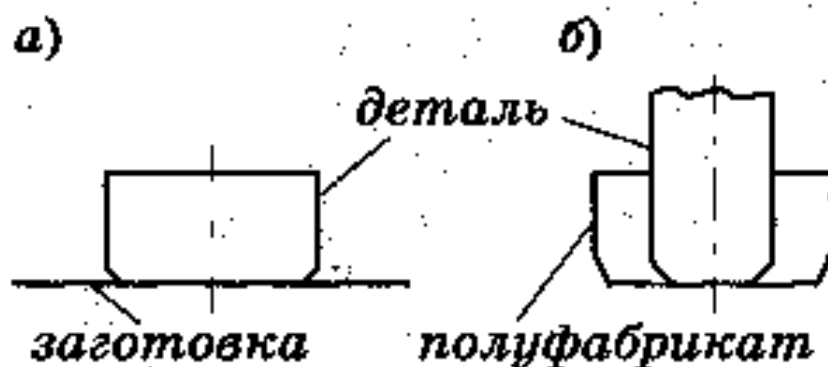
Схема вытяжки деталей: а) из плоской заготовки; б) из полый заготовки
